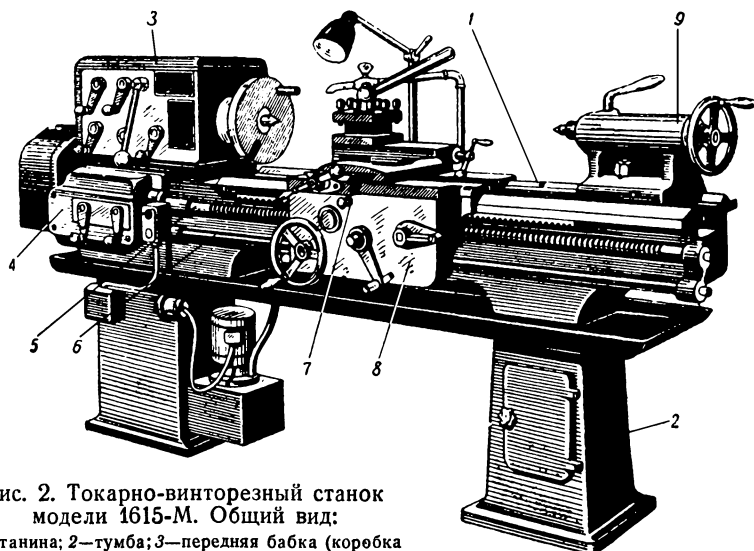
Токарно-винторезный станок модели 1615-М. Общий вид:
